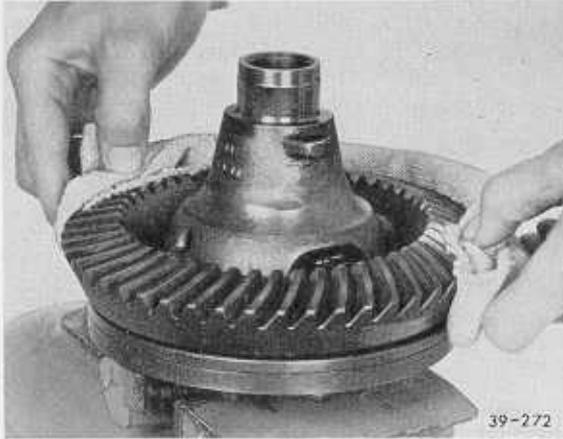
Tellerrad auf das Ausgleichgetriebe aufsetzen.
